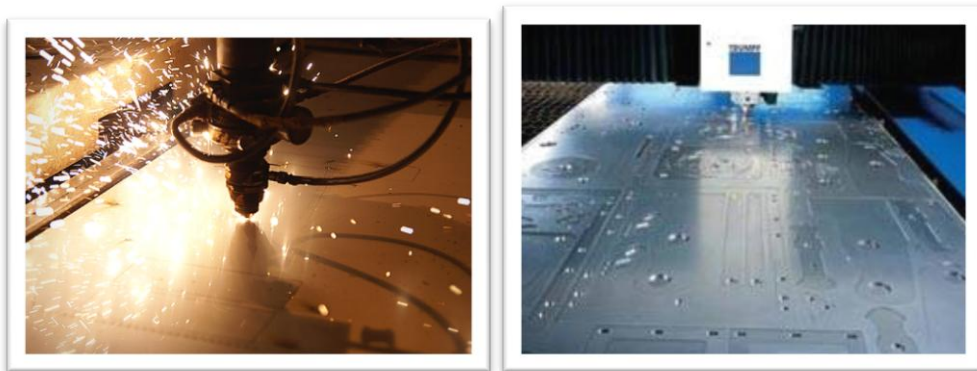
Резка лазером будущего корпуса электрической подстанции.
